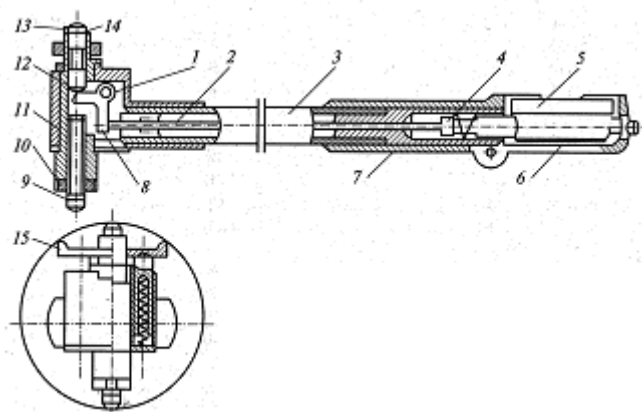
Конструкция индикаторного нутромера: 1 — ось вращения рычага; 2 — шток; 3 — трубка; 4 и 14 — пружина; 5 — отсчетное устройство (индикатор); 6 — предохранительный кожух; 7 — теплоизоляционная рукоятка; 8 — Г-образный рычаг; 9 — неподвижный (регулируемый) стержень; 10 — контргайка; 11 — корпус; 12 — шарик; 13 — подвижный (измерительный) стержень; 14 — риска; 15 — центрирующий мостик
